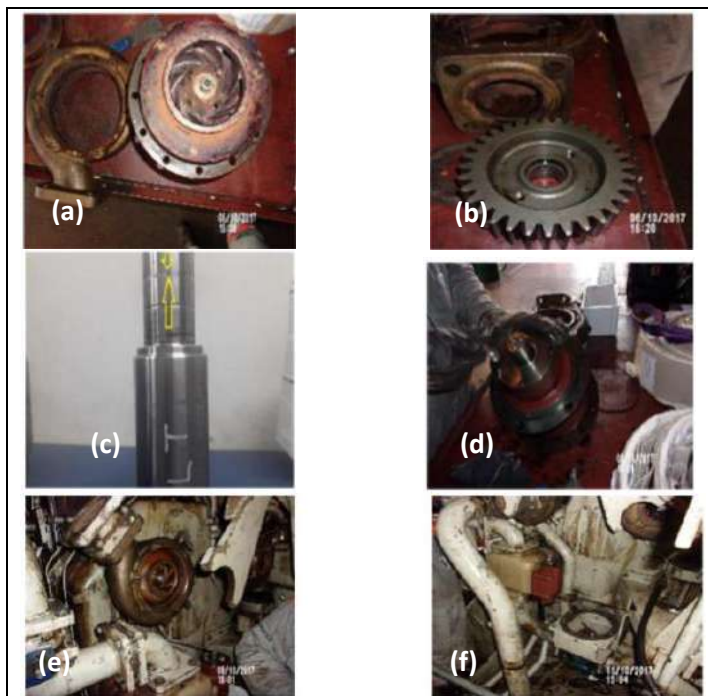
(a) Desmontagem; (b) Inspeção; (c) Eixo com desgaste na área do retentor; (d) Revisão da bomba; (e) Montagem da bomba; (f) Instalação e torque das tubulações de LT.
